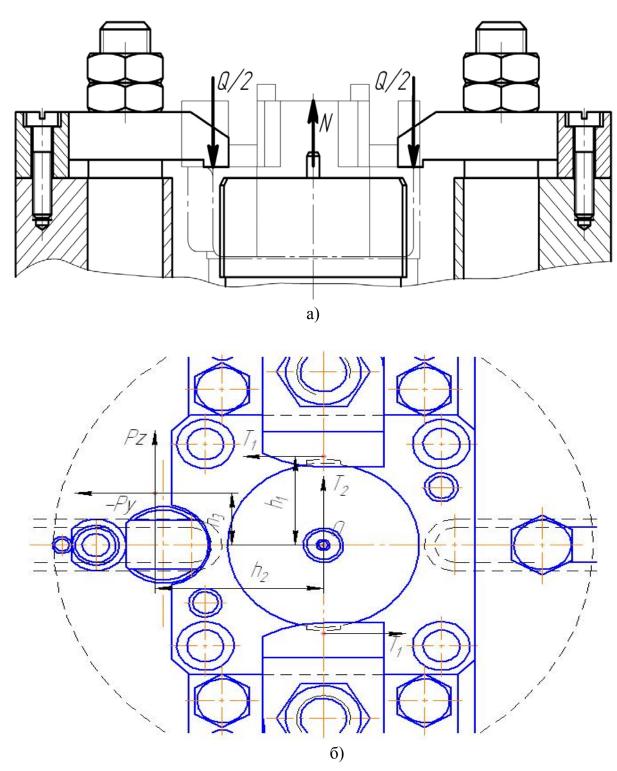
Схема закрепления заготовки и силовая нагрузка, приложенная к заготовке «Корпус»
